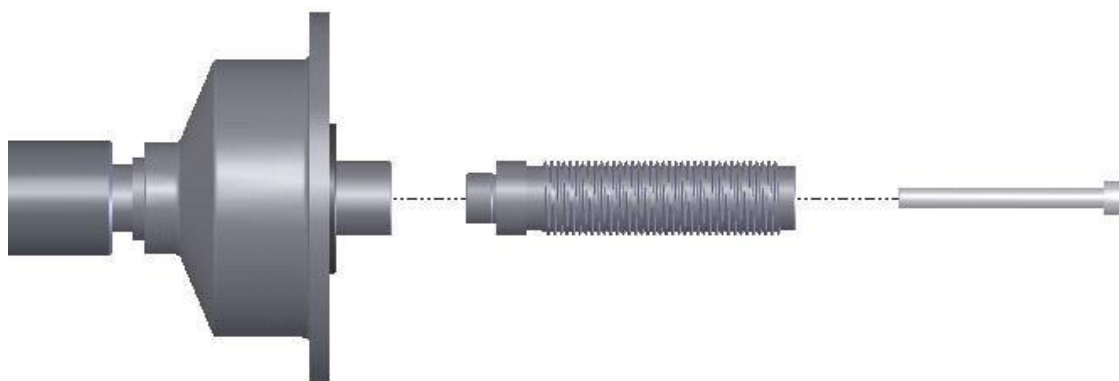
Адаптер типа конус для колес с центральным отверстием.
